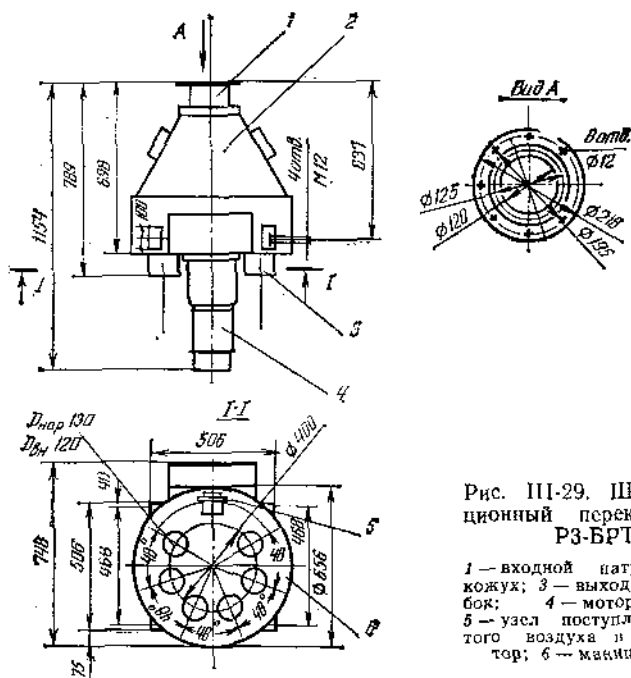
Шестипозиционный переключатель РЗ-БРТ:
